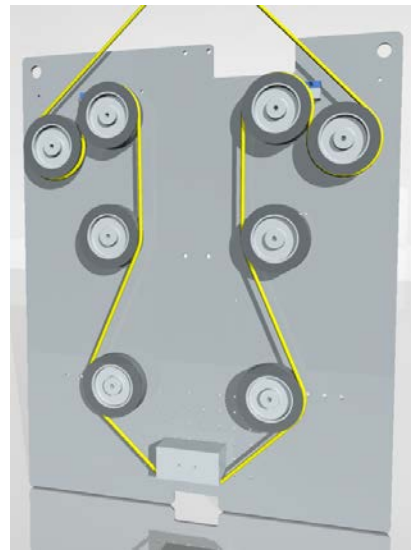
CAD Bild der Wechsellvorrichtung mit Seilführung
